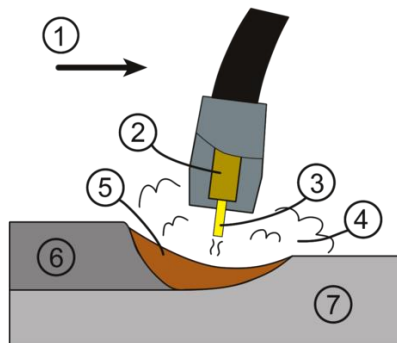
Proceso: 1. Dirección de la soldadura 2. Tubo de contacto 3. Hilo 4. Gas protector 5. Soldadura 6 y 7. Piezas a unir. [3]
